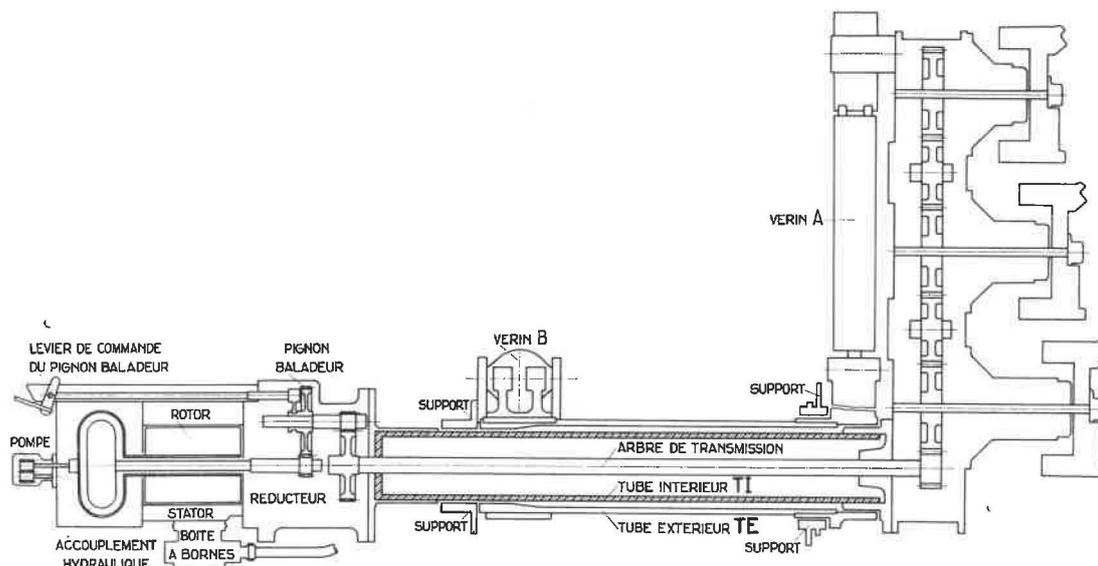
Schéma montrant l'ensemble des organes actifs de la machine à bosseyer - Moteur - Réducteur - Pompe - Arbre de transmission - Bras porte-outils et Vérins.
